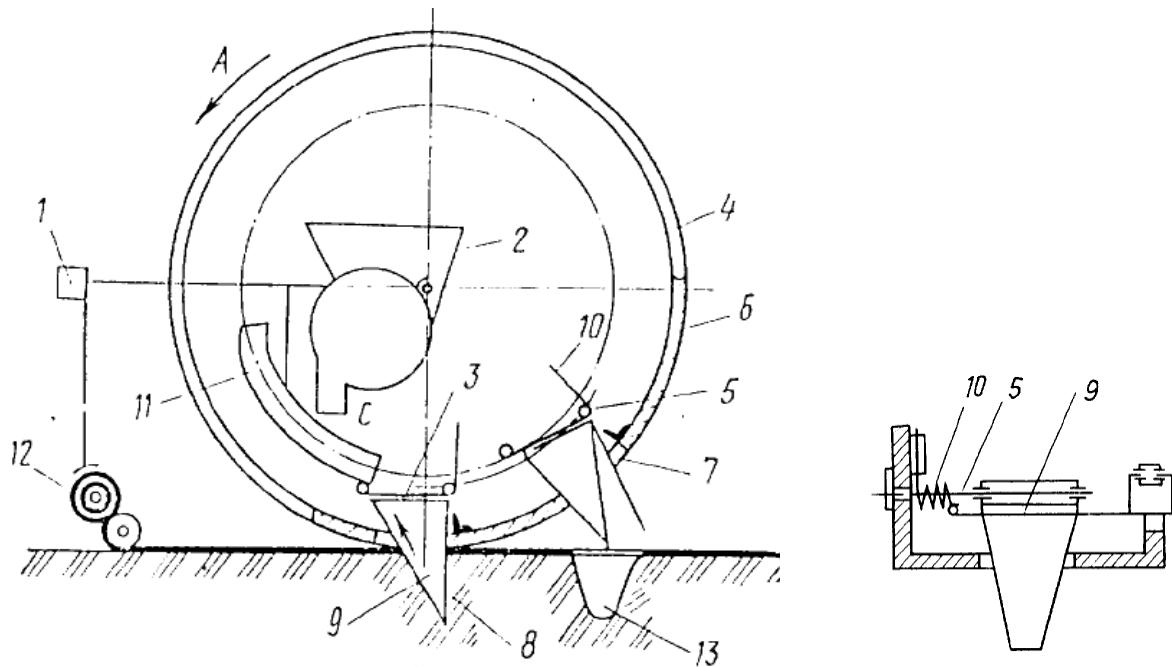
Сеялка для прокалывания пленки и высева семян в образовавшуюся лунку: 1-рама; 2-высевающий аппарат; 3-прокалыватель пленки; 4-перфорирующее колесо; 5-ось; 6, 7, 8-задняя часть ковша; 9-передняя часть ковша; 10-пружина; 11-направитель; 12-пленкоукладчик; 13-семя
